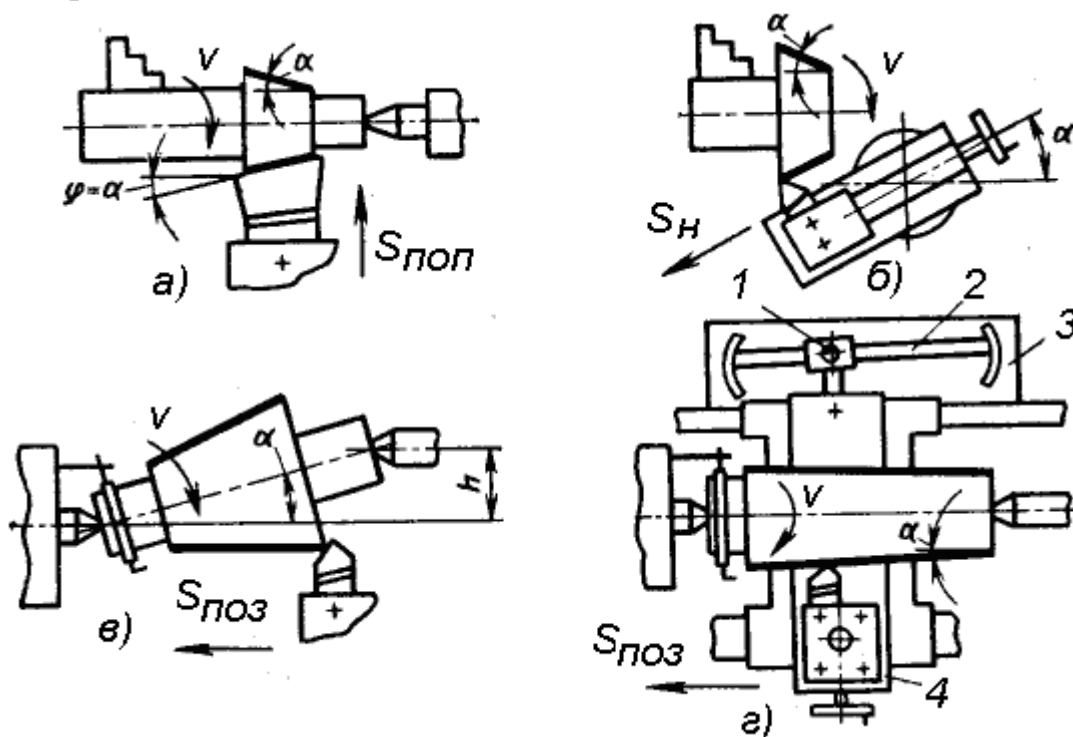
Схеми обточування зовнішніх конічних поверхонь на токарних верстатах
